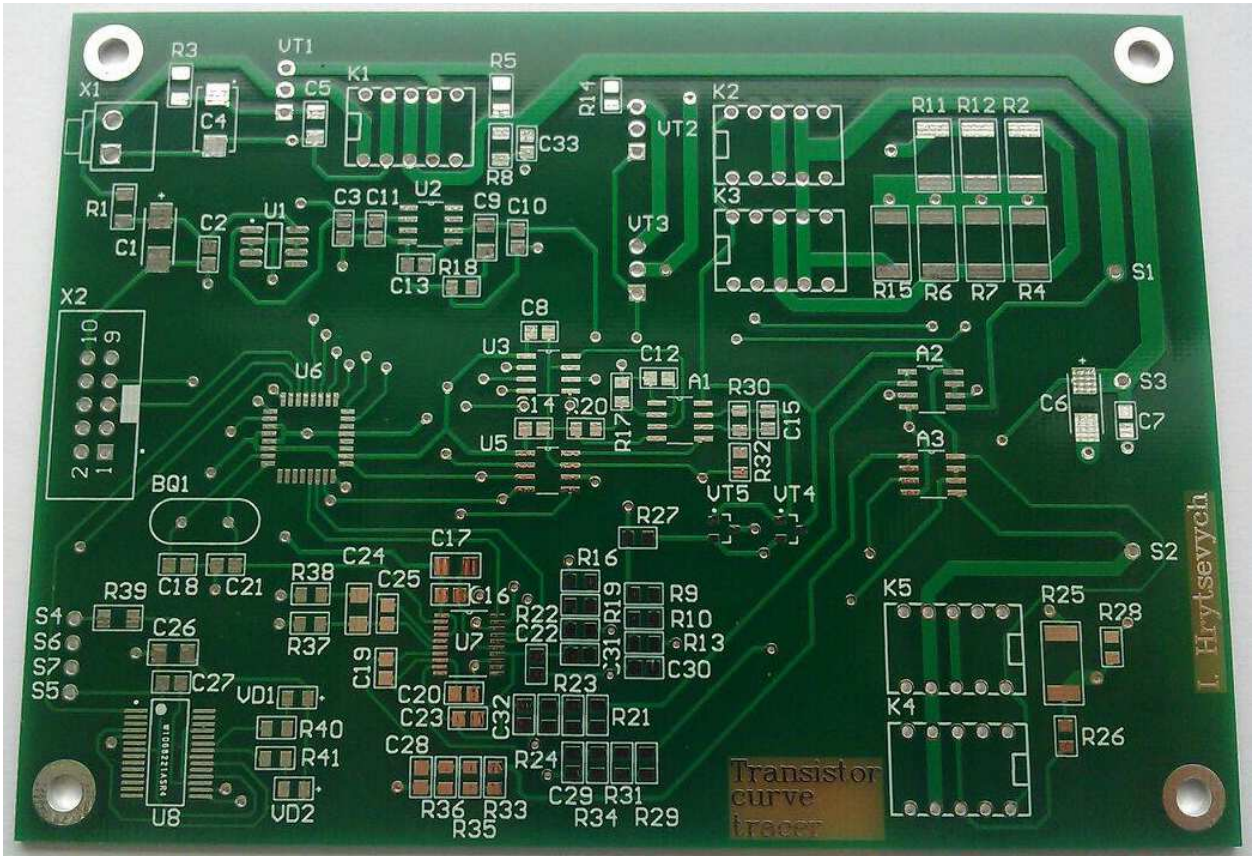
Виготовлена друкована плата пристрою (вид зверху)
